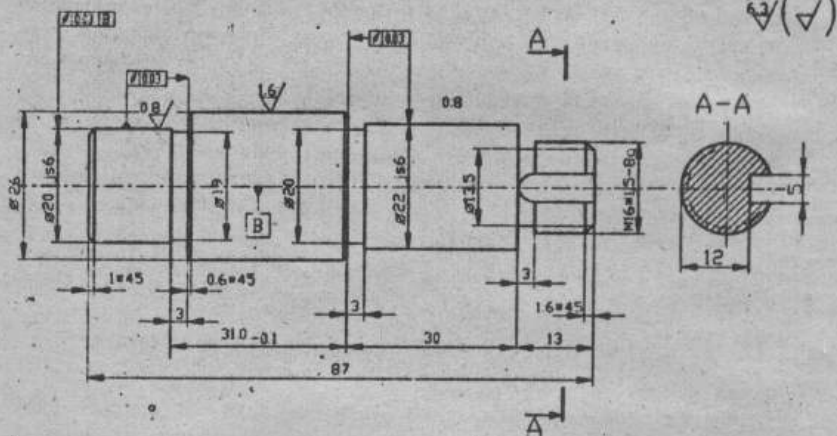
Вал (вид заготовки-прокат, материал-сталь 45,
